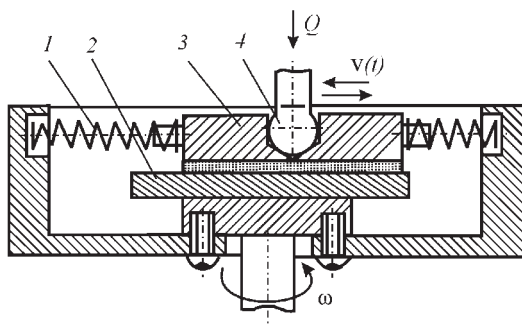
Схема устройства для стабилизации скорости относительного движения инструмента и заготовки
